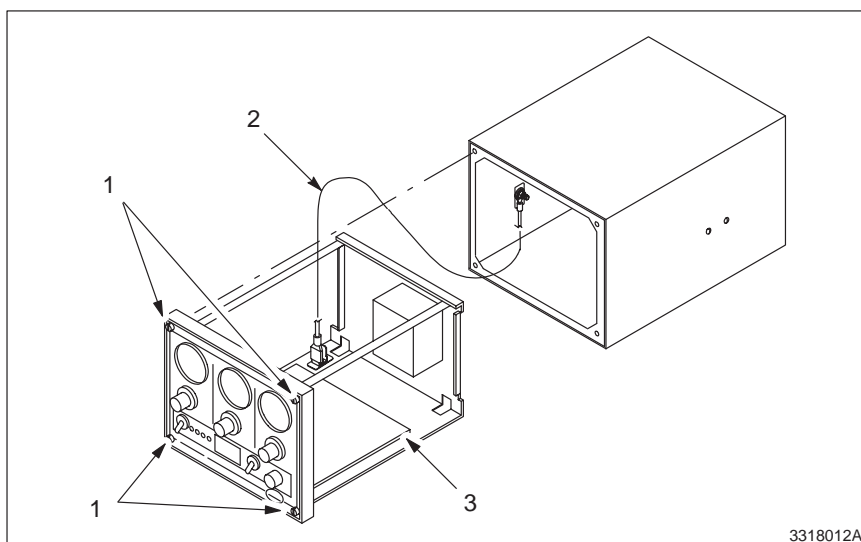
Steuermodul aus dem Gehäuse ausbauen
